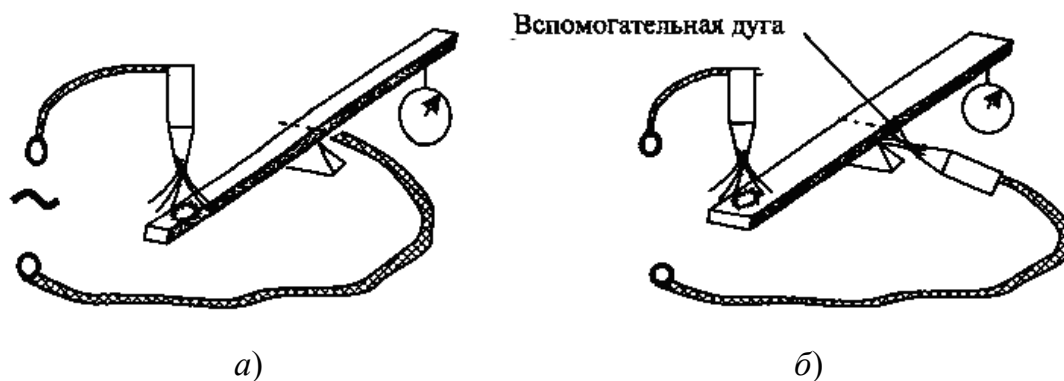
Схемы для измерения давления сварочной дуги:
